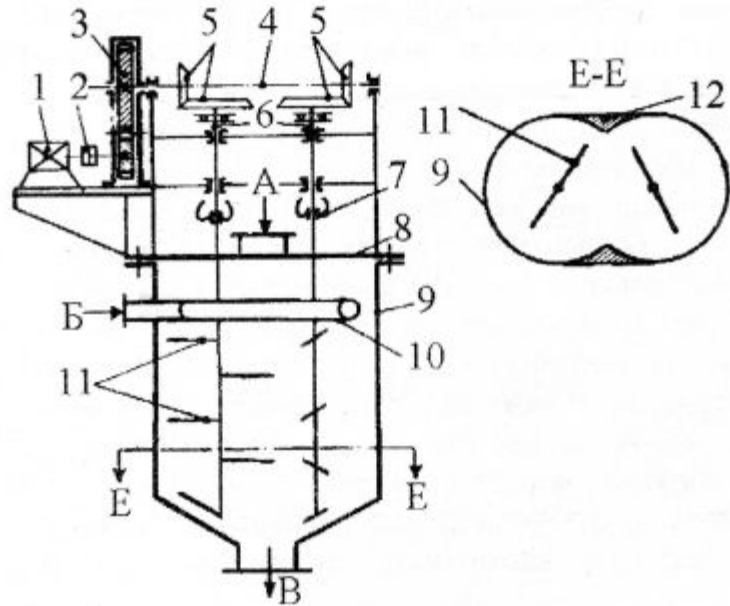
Нитратор - дозер. 1 - электродвигатель, 2 - соединительная муфта, 3 - зубчатая передача, 4 - горизонтальный вал, 5 - конические передачи, 6 - вертикальные валы, 7 - маслоуловитель, 8 - крышка, 9 - корпус аппарата, 10 - ороситель, 11 - лопастные мешалки, 12 - гребешок; А - подача целлюлозы, Б - подача РКС, В - выгрузка реакционной массы
